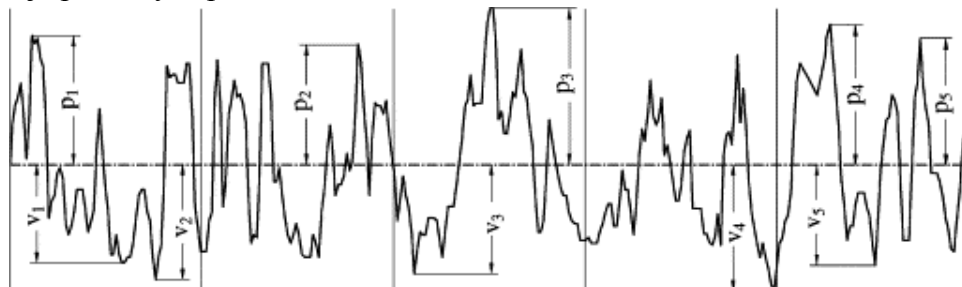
Střední vzdálenost výšek elementů profilu [8]
